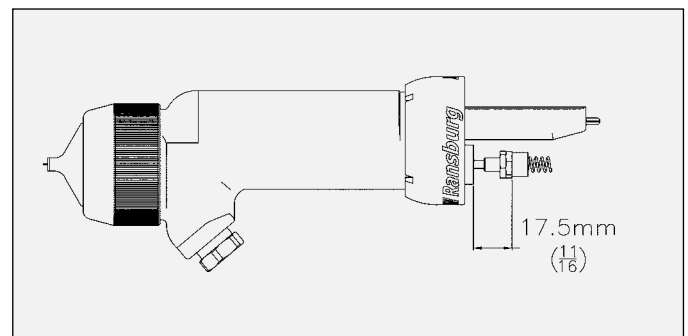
Dimensions de l'écrou de réglage de gâchette
